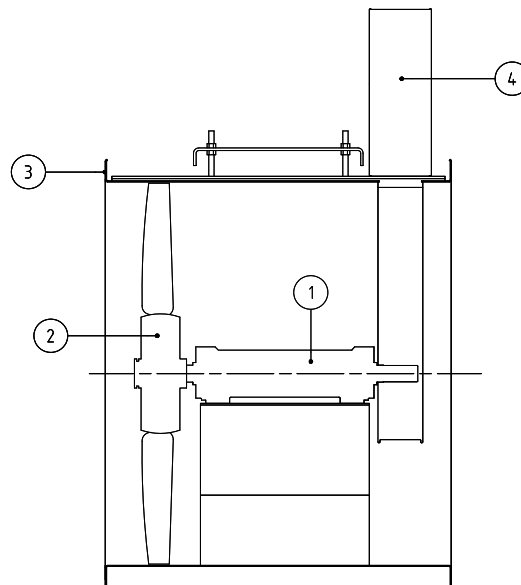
Zusammenbau des Axialventilators in Ausführung 1
